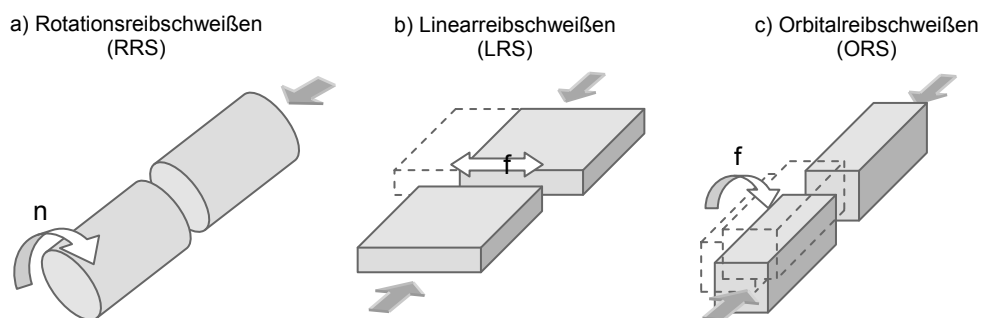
Reibschweißverfahren: Rotations-, Linear- und Orbitalreißschweißen
